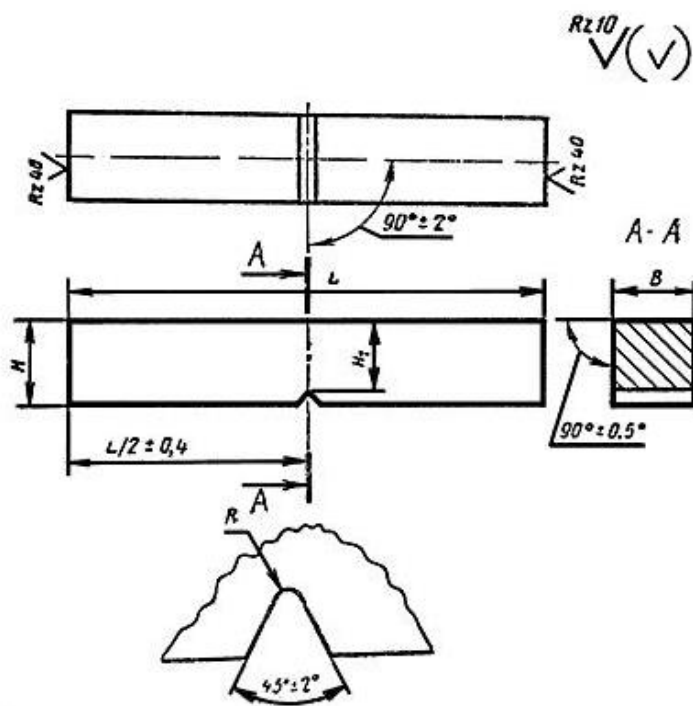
Образец для испытания на ударный изгиб с концентратором вида V
